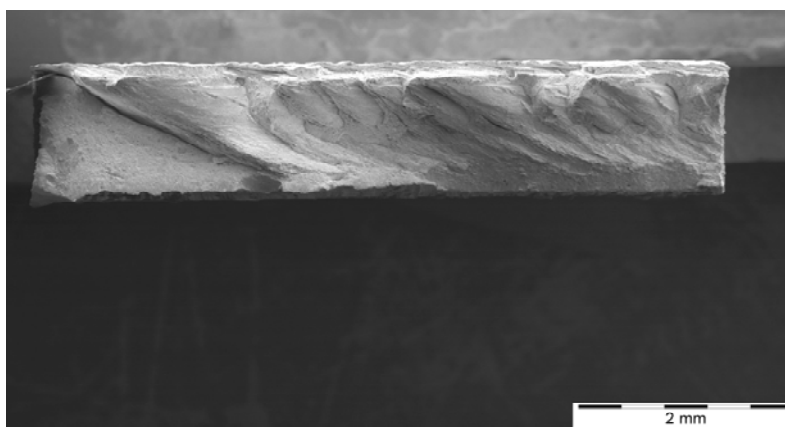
Superfície de fratura da junta soldada da liga 2024-T351, após ensaio de corrosão sob tensão, com taxa de deformação 10^{-6} s^{-1} , ao ar.
